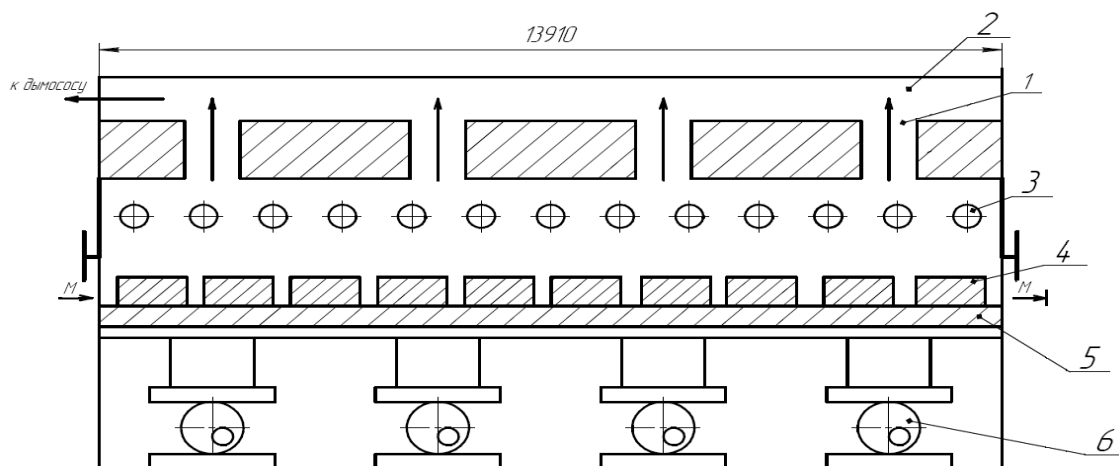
Схема печи: 1 – дымовые каналы; 2 – общий дымопровод; 3 – горелки ВИС 140; 4 – нагреваемый металл; 5 – под с шагающими балками; 6 – механизм передвижения пода
